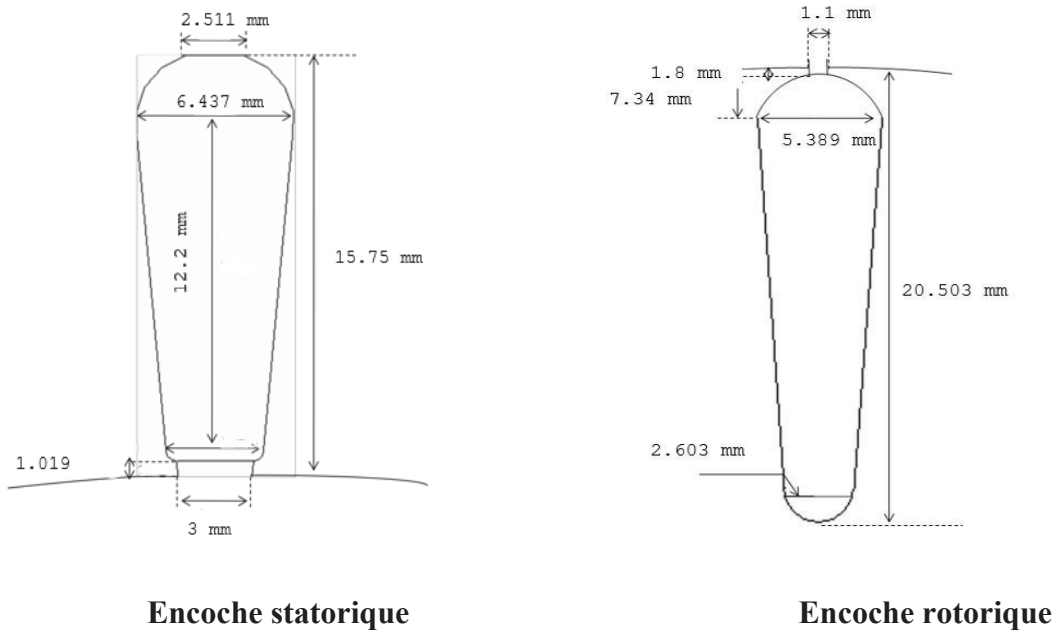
Dimensions et formes des encoches statorique et rotorique.
